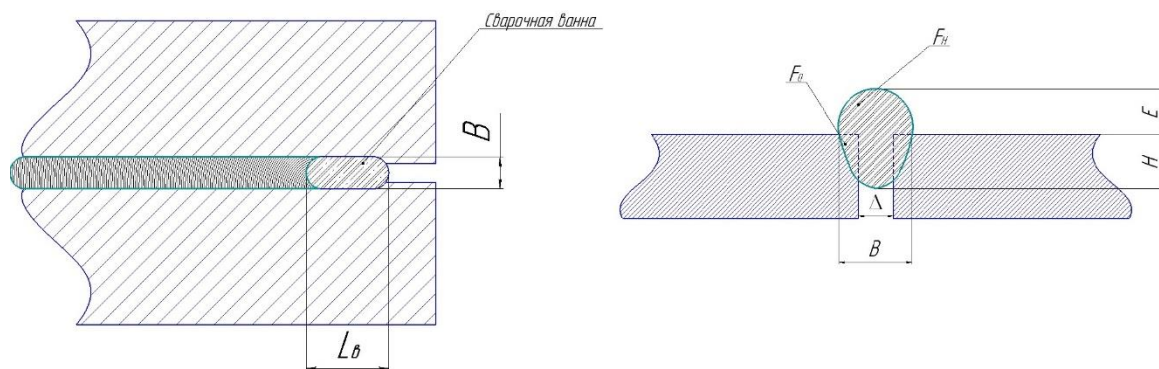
Формы сварочной ванны при дуговой сварке
